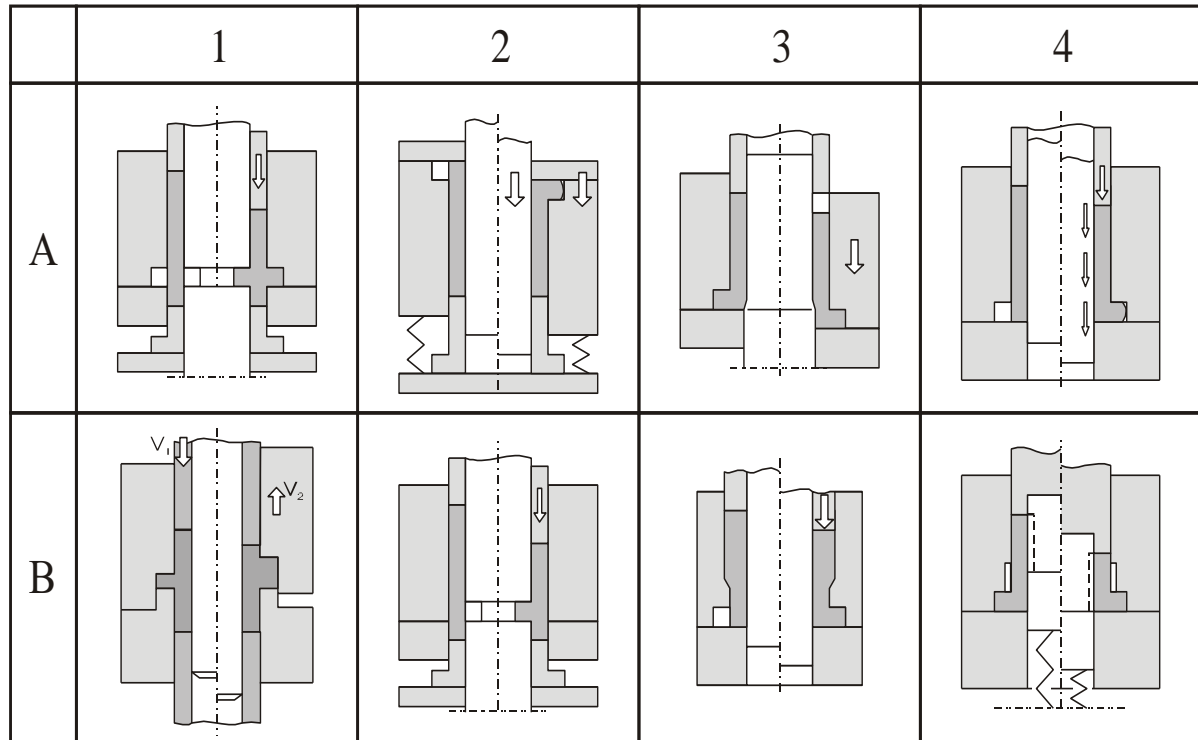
Способи видавлювання деталей типу втулок із фланцем
